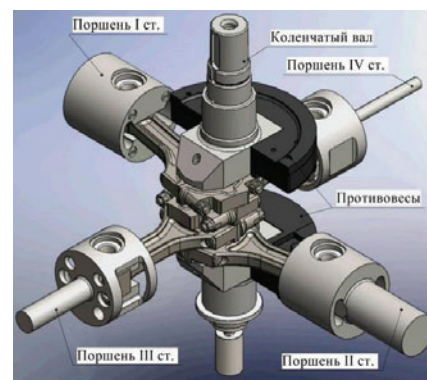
Механизм движения четырехрядного компрессора с вертикальным коленчатым валом
